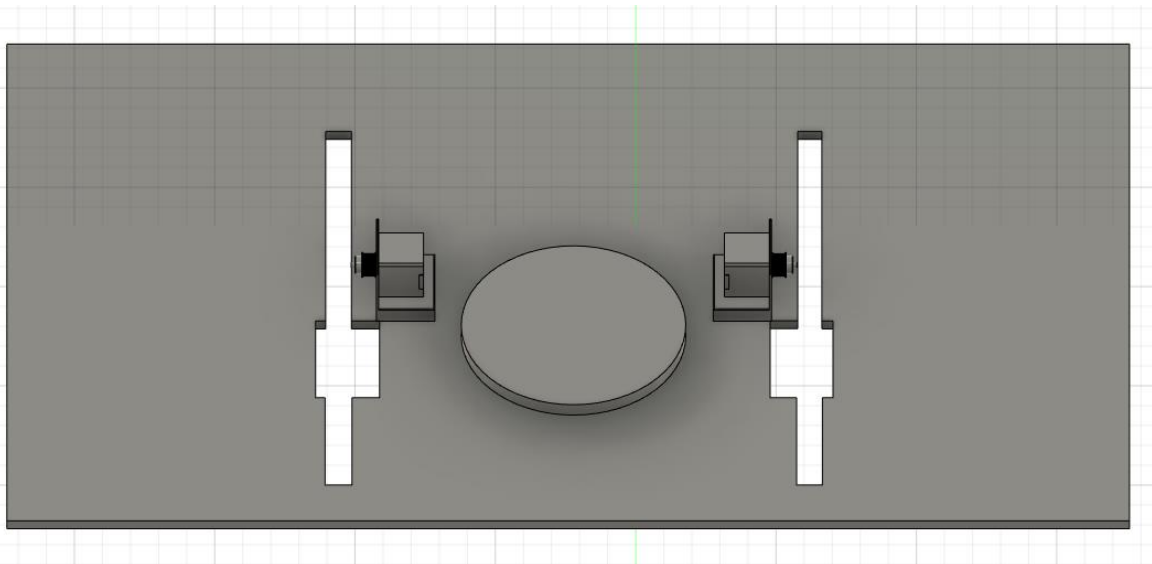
Інший вид на 3D-модель механічної конструкції робочої поверхні
